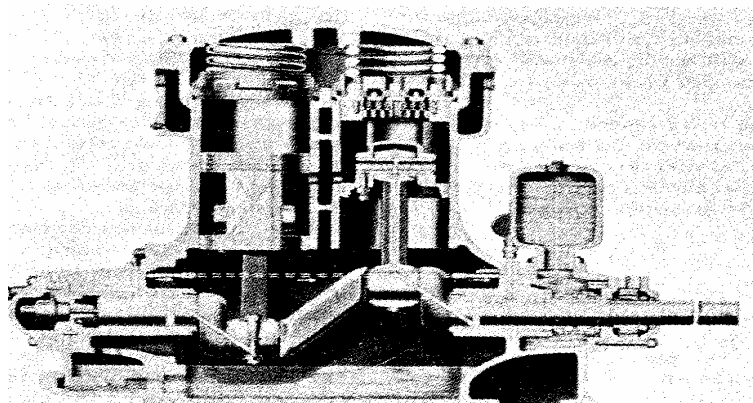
Compresor Vertical de acción simple. (Cortesía de Vilter Manufacturing Company).
